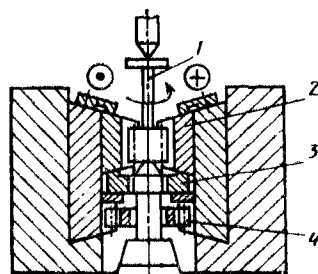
Схема калибровки эвольвентных шлицев:
